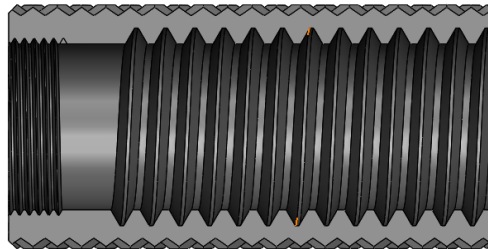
Vista em corte do elemento central (Modelo 3D).
